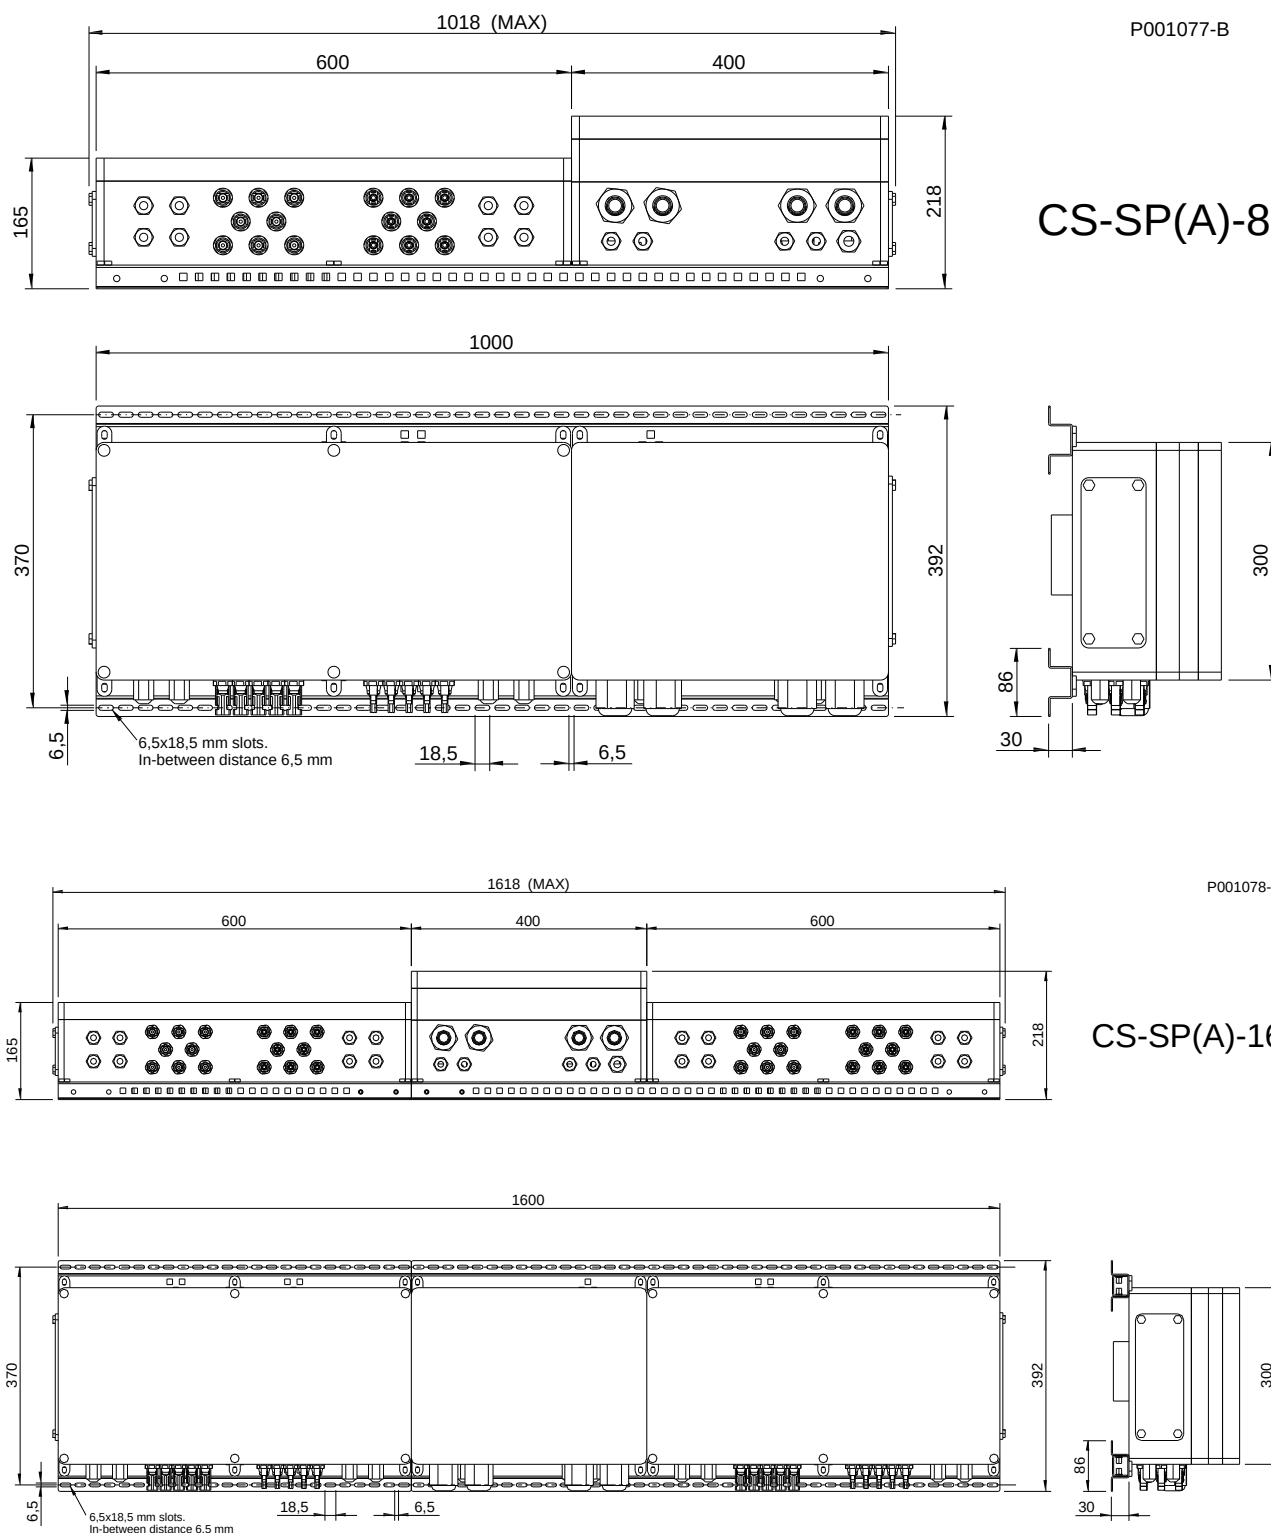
Размеры стандартного коммуникатора SMART STRING BOX.
